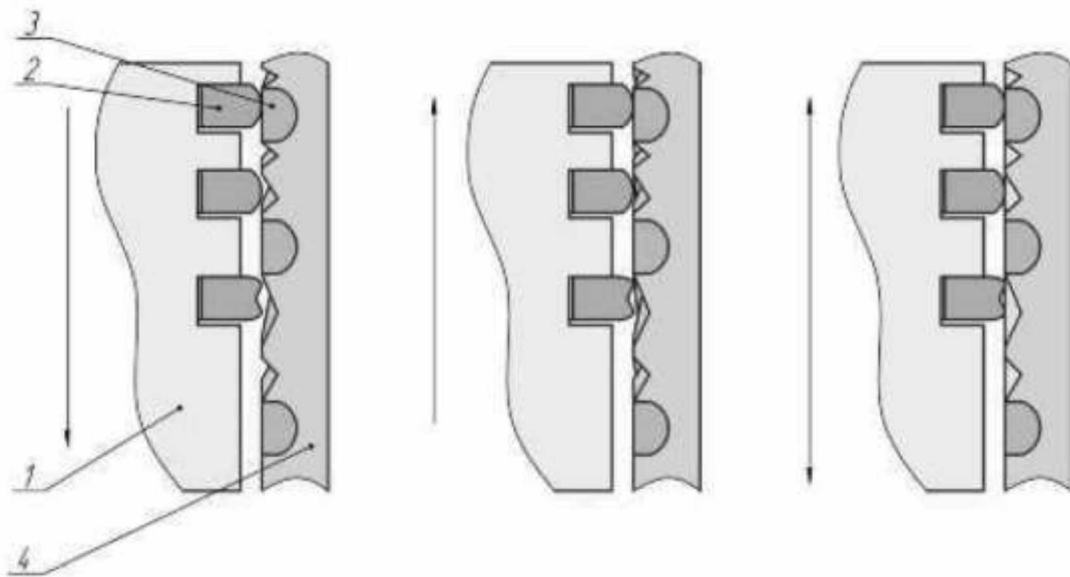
Схема формування плівки кольорового металу на поверхні тертя гільзи циліндрів: 1 – поршень; 2 – поршкові кільця; 3 – канавка; 4 – гільза циліндрів
